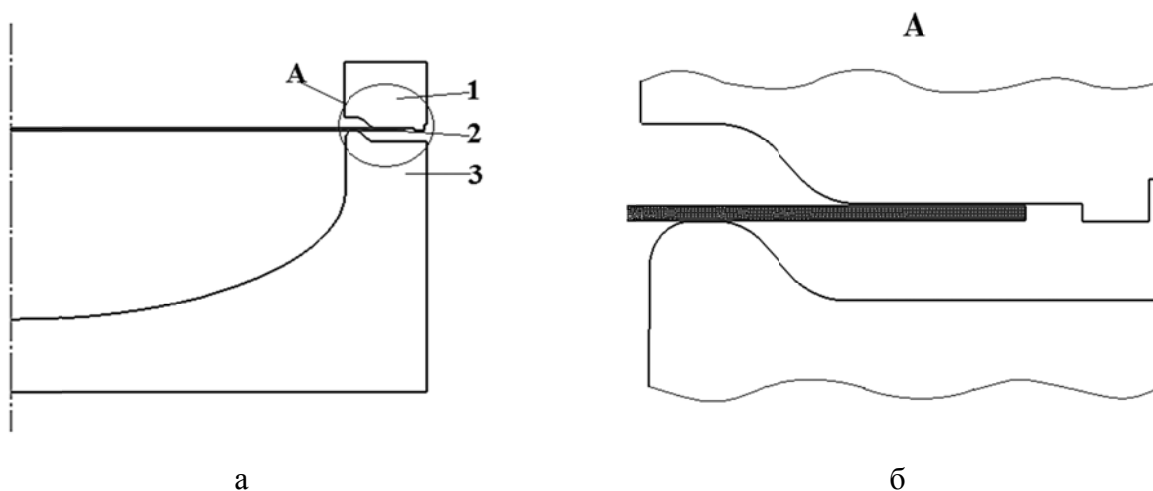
Схема деформирования заготовки в области прижимного кольца:
